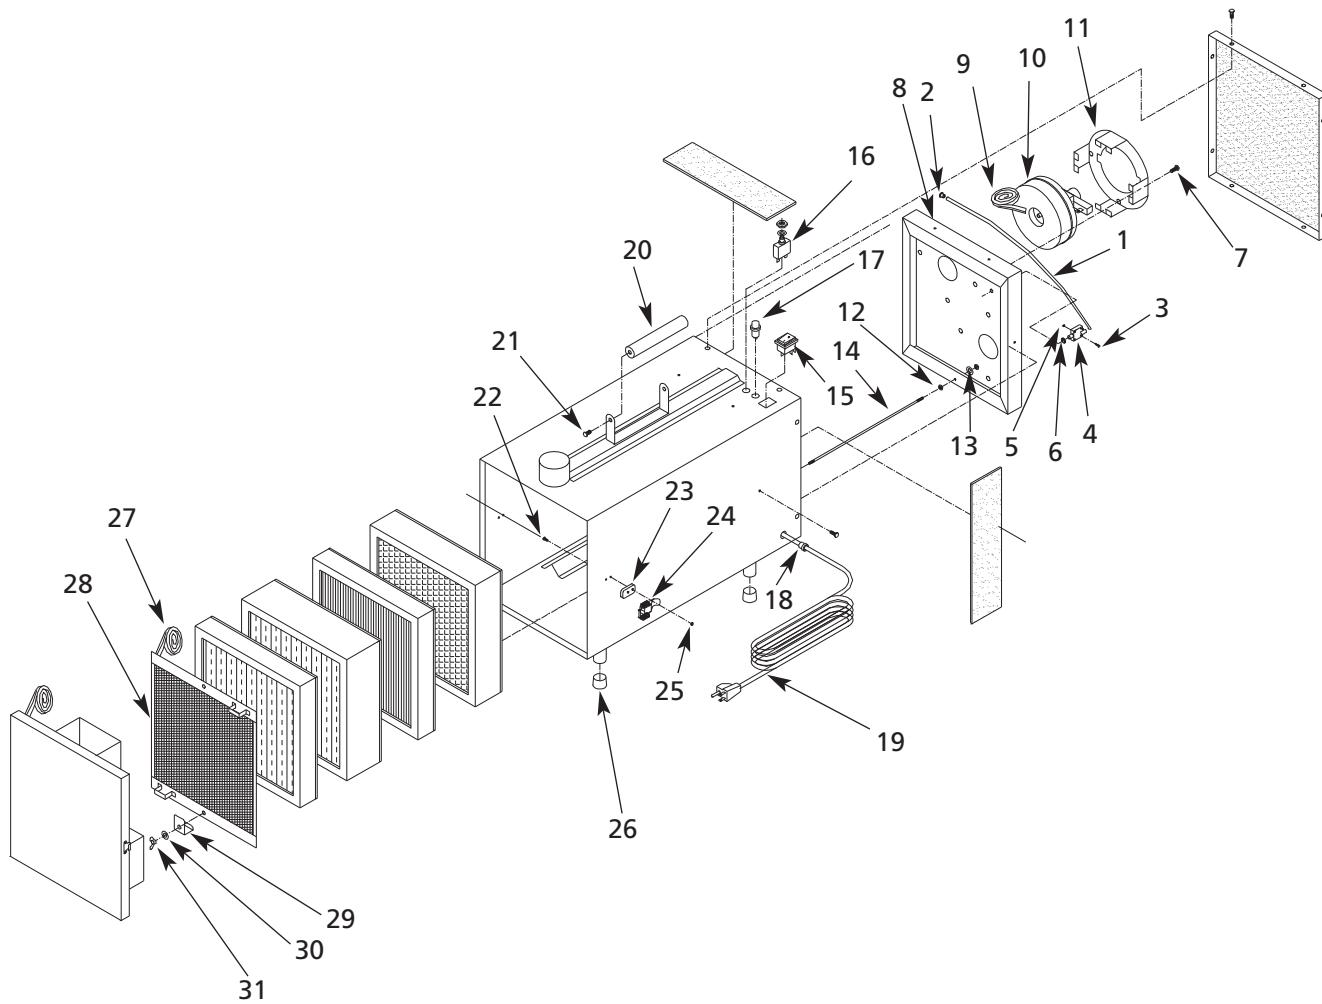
Illustration des pièces détachées pour l'extracteur d'émanation de soudure portable
